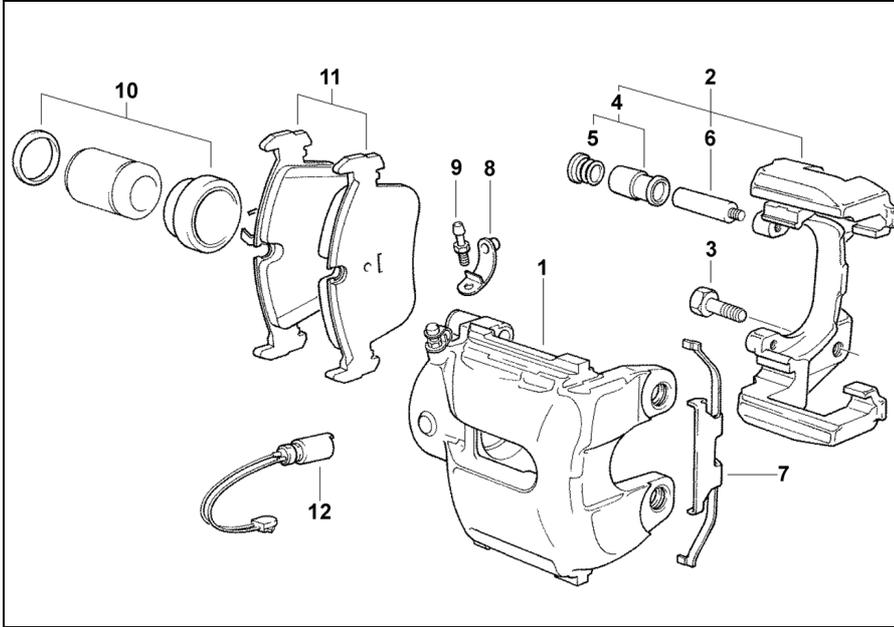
Тормозной механизм передних колес. 1 - корпус суппорта, 2 - направляющая тормозных колодок, 3 - болт (M12x1,5x41), 4 - направляющая втулка, 5 - пробка, 6 - направляющий палец, 7 - фиксирующая пружина, 8 - пылезащитный колпачок, 9 - штуцер для прокачки, 10 - уплотнители, 11 - тормозные колодки, 12 - датчик износа.
